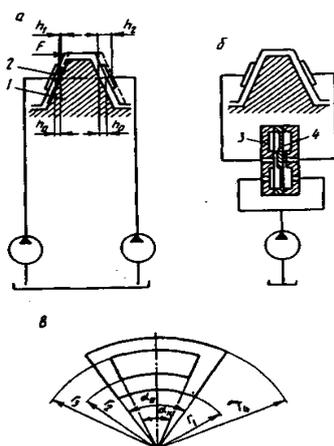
Схема гидростатической червячно-реечной передачи
